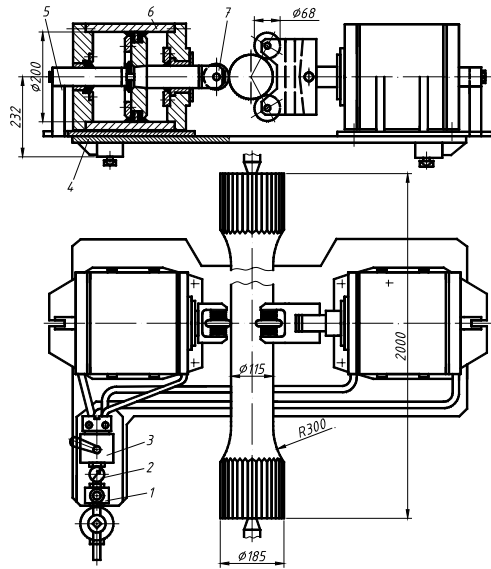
Приспособление для обкатывания торсионных исчезающих упоров прокатных станов
